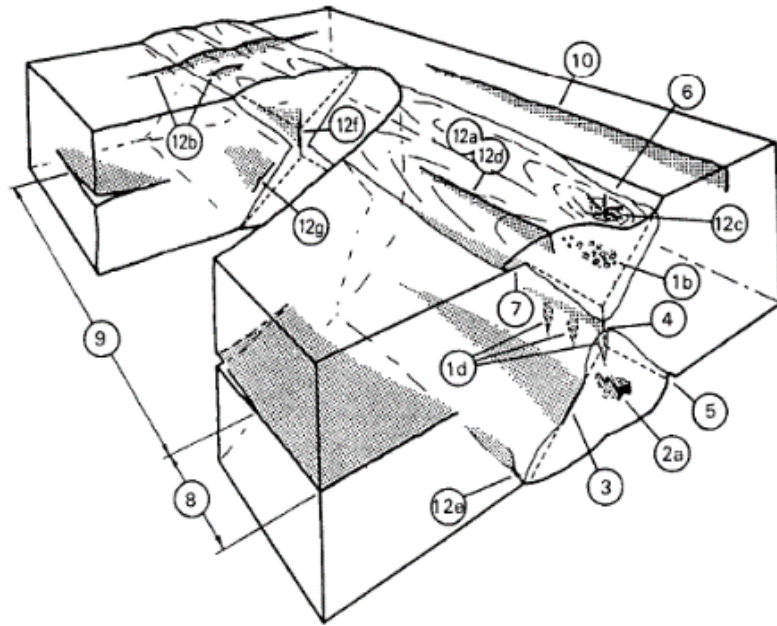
14 Soldadura ranura en doble V con unión a tope (14)
